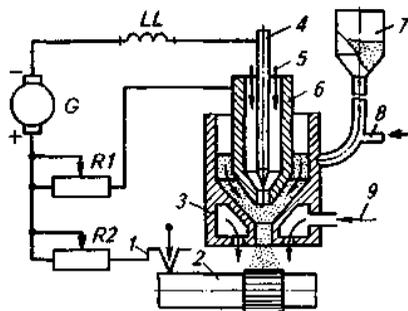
Схема наплавки с вдуванием порошка в плазменную струю:
